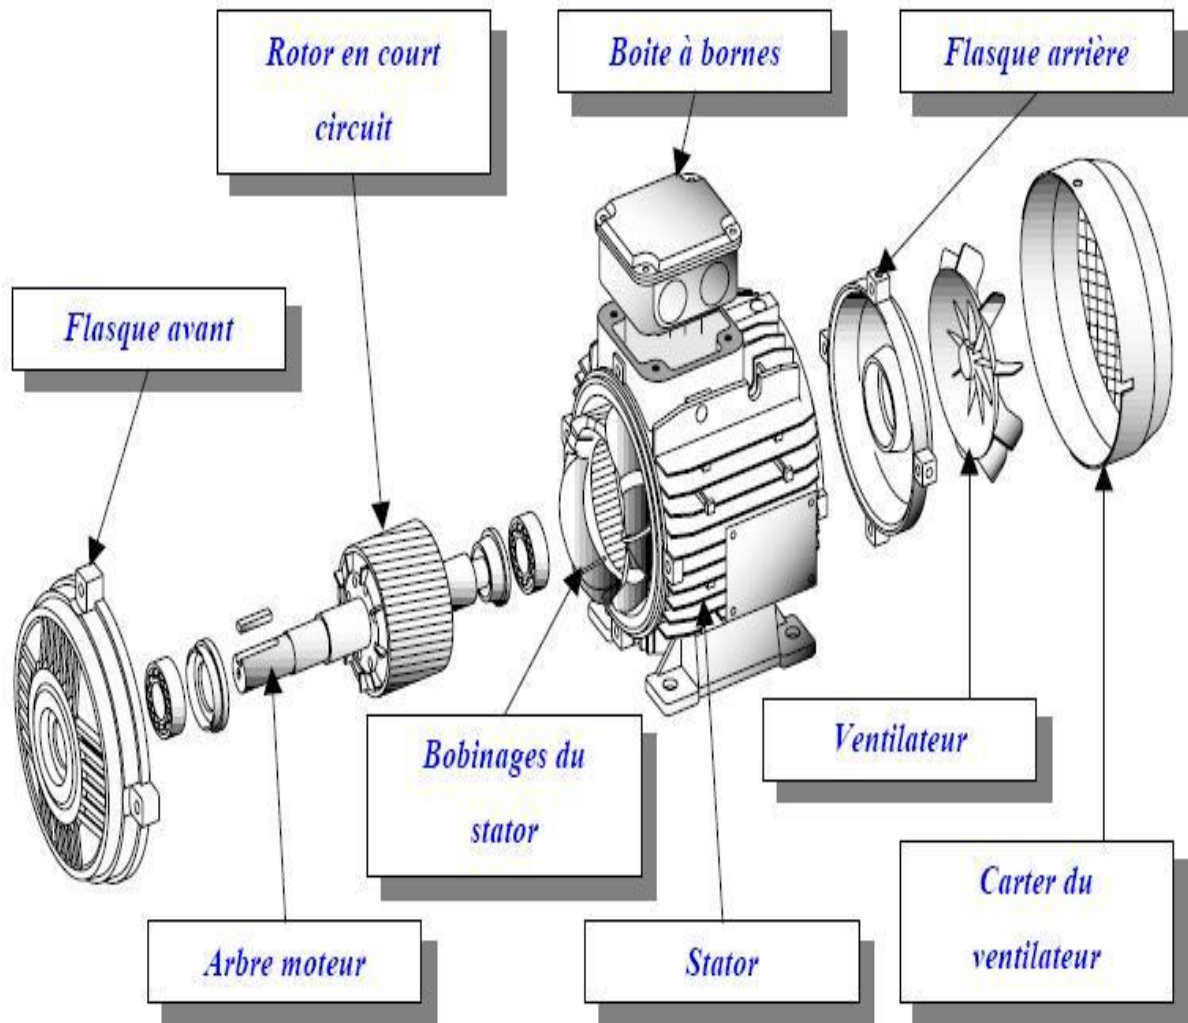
Vue éclaté de la machine asynchrone [14].
